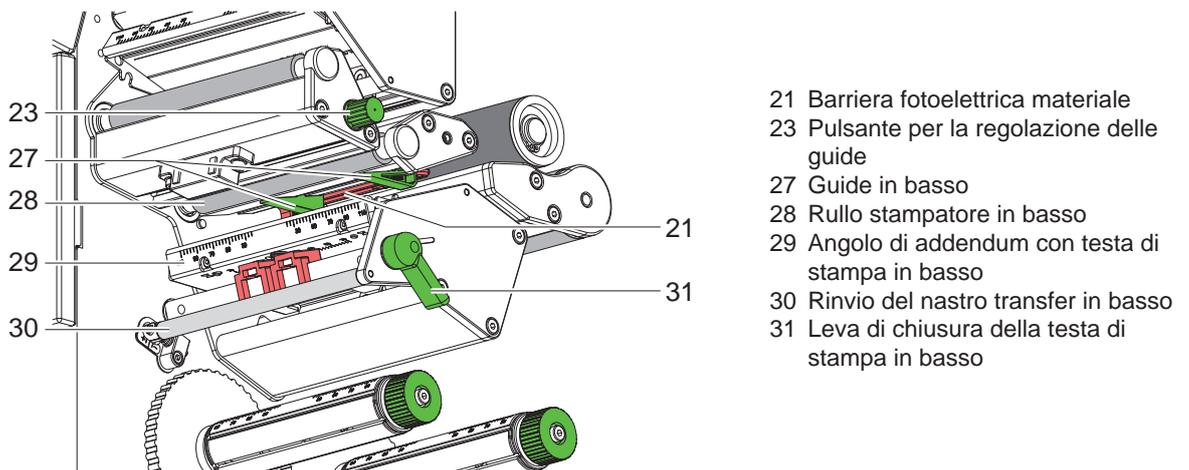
Meccanica di stampa - gruppo inferiore stampante
